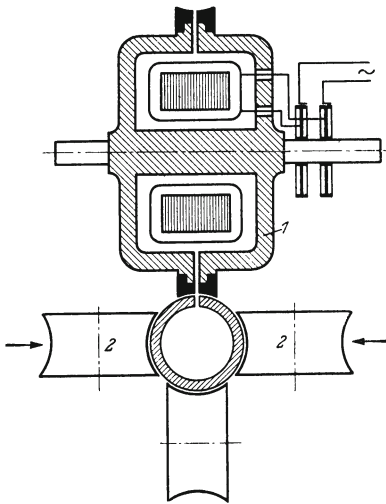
Rohrnahtschweißmaschine. Der Stoß wird durch den Ringumspanner 1 erhitzt. Die Rollen 2 erzeugen den Schweißdruck.
